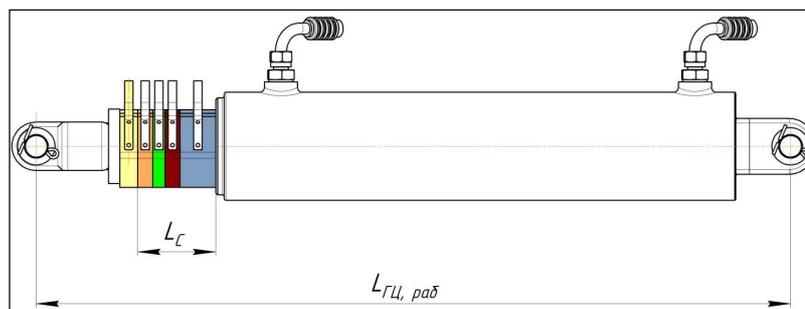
Установка стоп-сегментов на шток гидроцилиндра шасси
